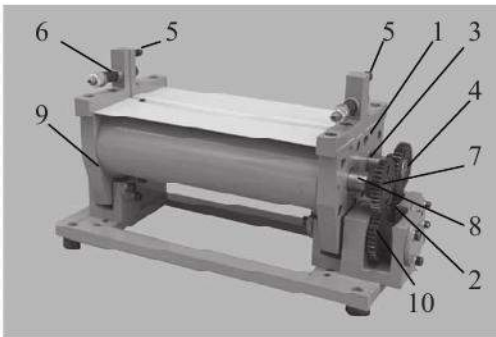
Вальцовий плющильний механізм: 1 – нерухома стійка; 2, 10 – проміжні шестерні; 3 – ведучий валік; 4 – шестерня ведучого валіка; 5 – регулювальний гвинт; 6 – пружинний механізм; 7 – шестерня веденого валіка; 8 – ведений валік; 9 – рухома стійка
